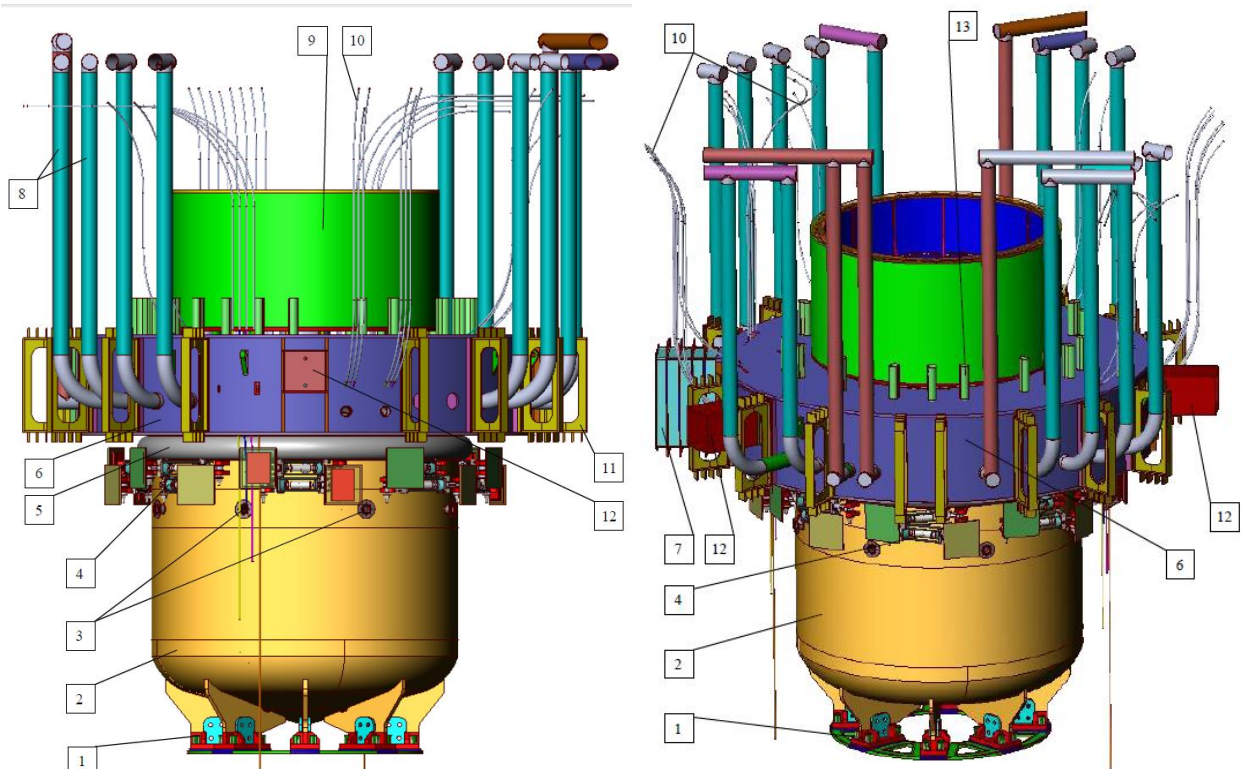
Устройство локализации расплава корпуса реактора в сборе
